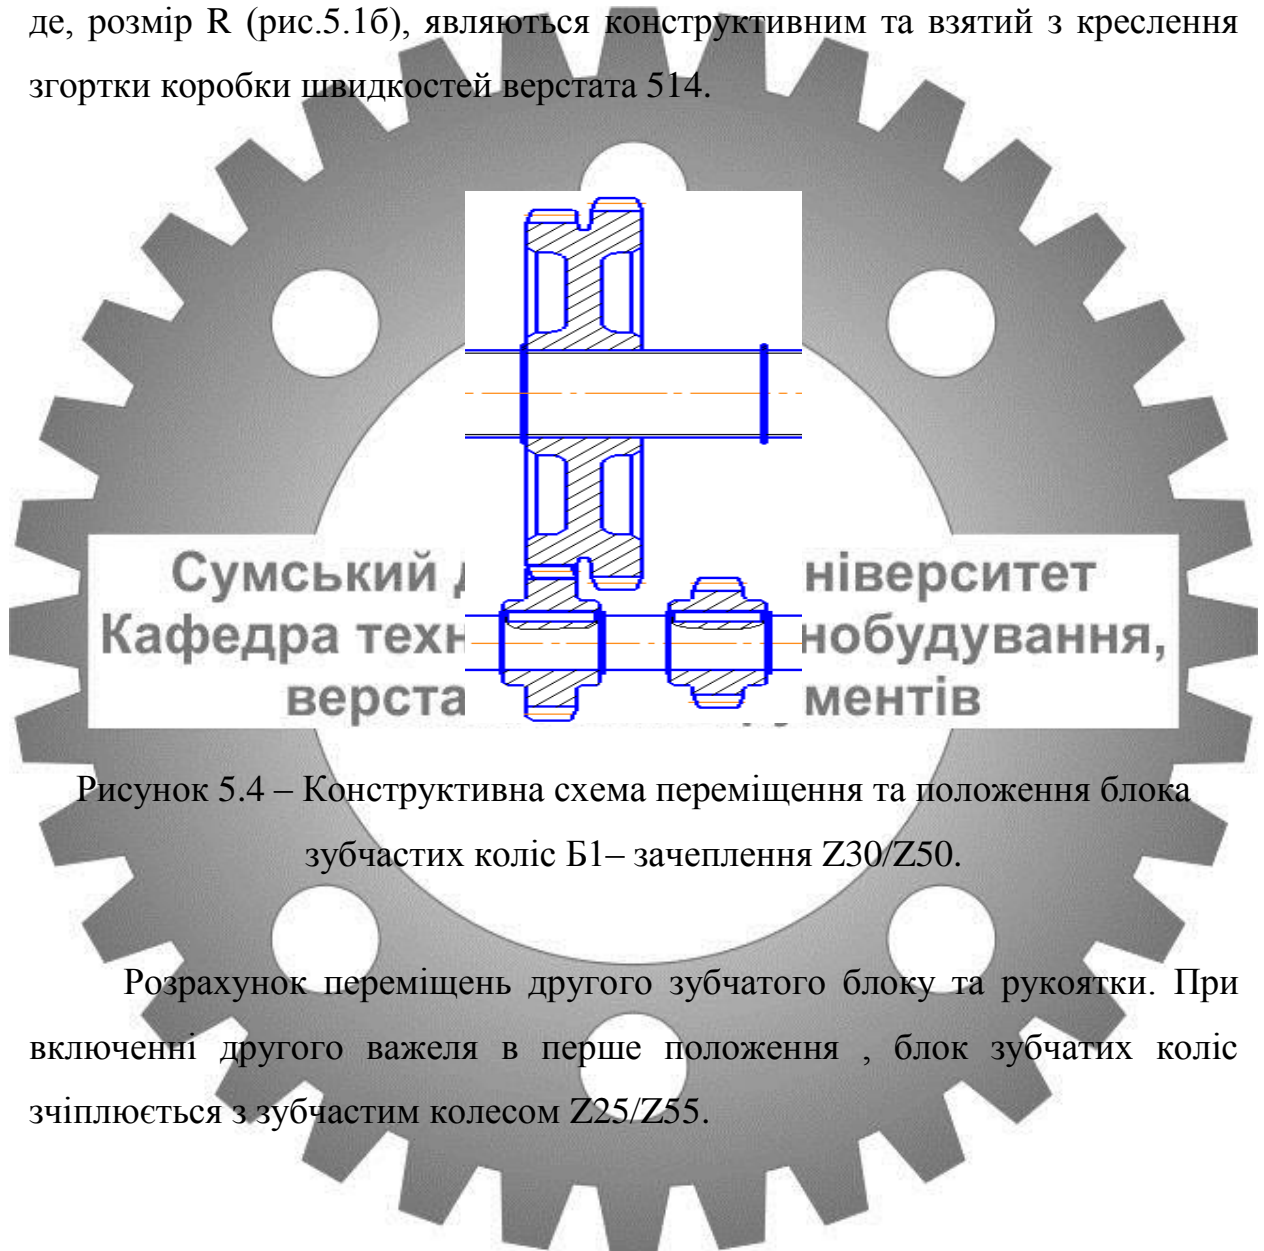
Конструктивна схема переміщення та положення блока зубчастих коліс Б1– зачеплення Z30/Z50.
